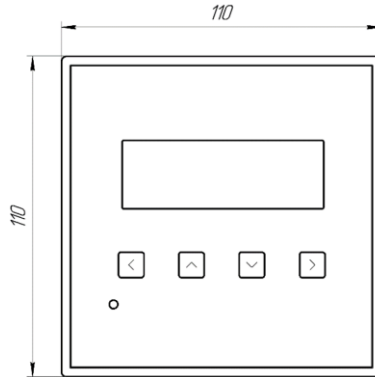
Габаритный чертеж устройства серии МСТ. Вид спереди
